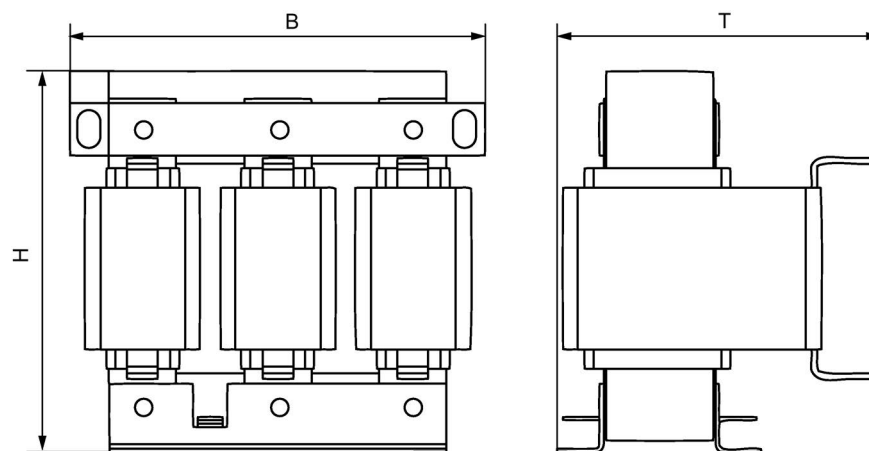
Croquis acotado de la bobina de motor 6SE4000-3TC...D0, para dimensiones ver tabla siguiente
